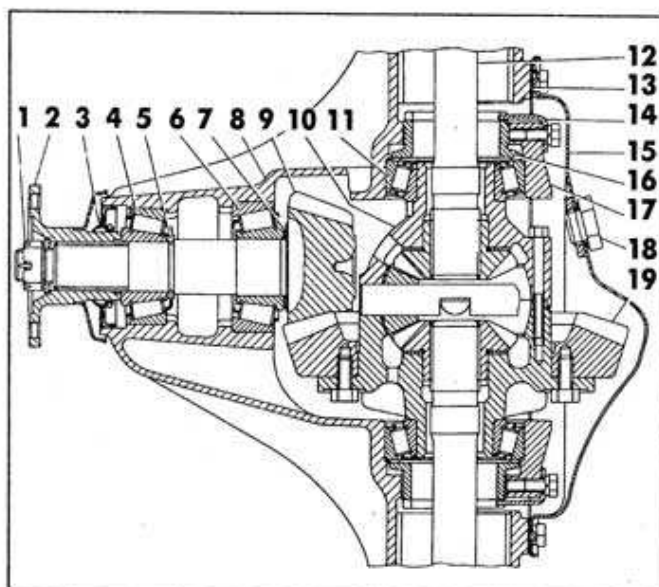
Неразъемный задний мост (средняя часть): 1 - гайка; 2 - фланец ведущей шестерни; 3 - манжета; 4, 6, 11 - подшипники; 5 - кольцо; 7 - регулировочное кольцо; 8 - картер; 9 - ведущая шестерня; 10 - дифференциал; 12 - полуось; 13 - прокладка крышки; 14 - стопорная пластина; 15 - крышка картера; 16 - гайка подшипников дифференциала; 17 - крышка подшипника дифференциала; 18 - пробка маслосливного отверстия; 19 - ведомая шестерня
